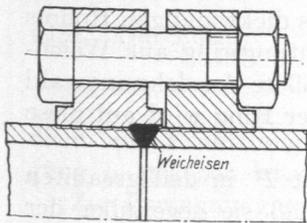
a. Rohrverbindung an Dampfleitungen bis zu 100 at Betriebsdruck.
